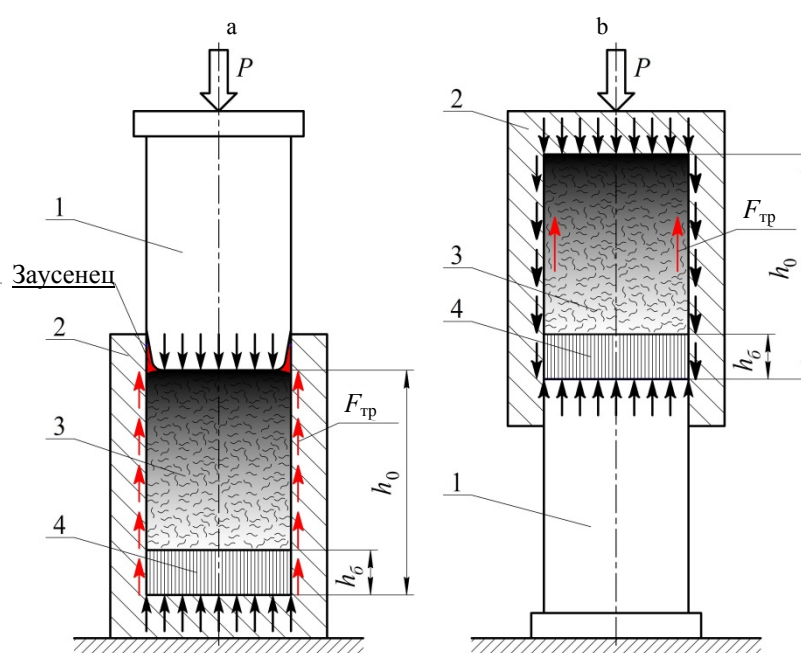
Схемы прессования стружки черных металлов в пресс-форме: а – с неподвижной матрицей; б – с подвижной матрицей
